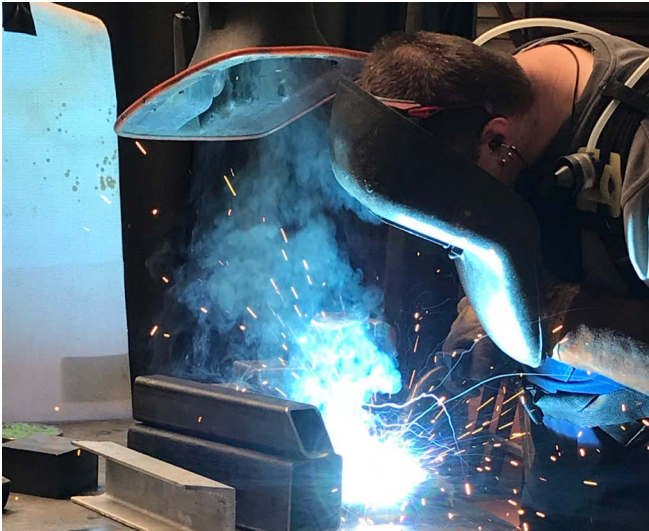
Saugrohr mit Düsenplatte für Schweißbrauche
